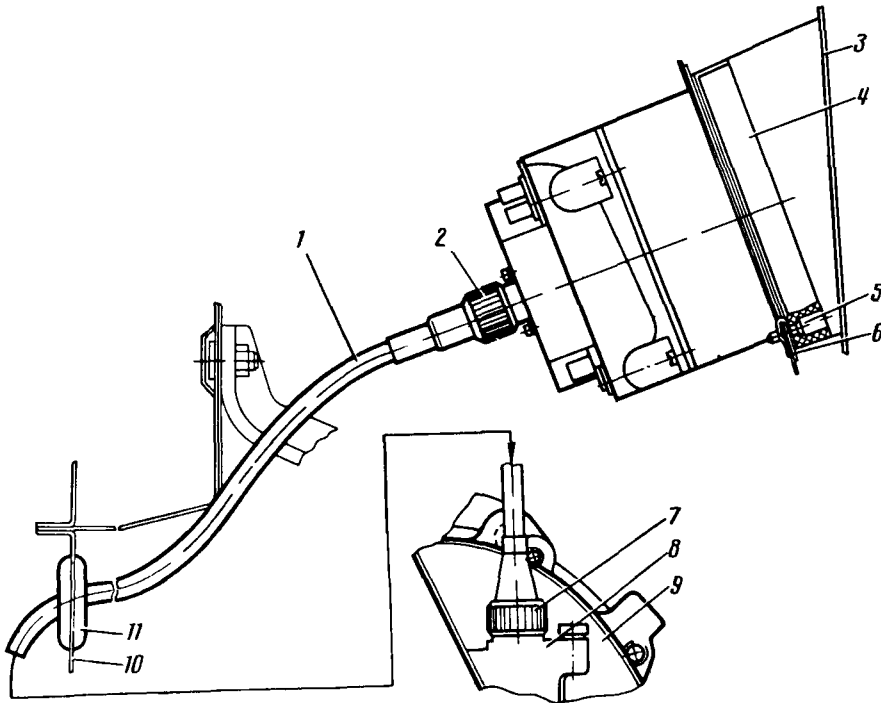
Гибкий вал спидометра, комбинация приборов и их крепление:
